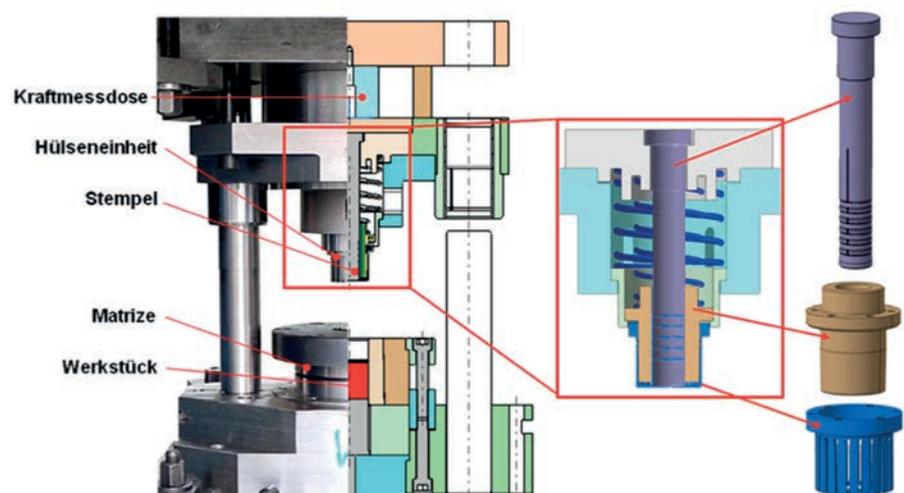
Stempelführung mit aktiver Zentrierhülse im Werkzeug für das Napf-Rückwärts-Fließpressen.
